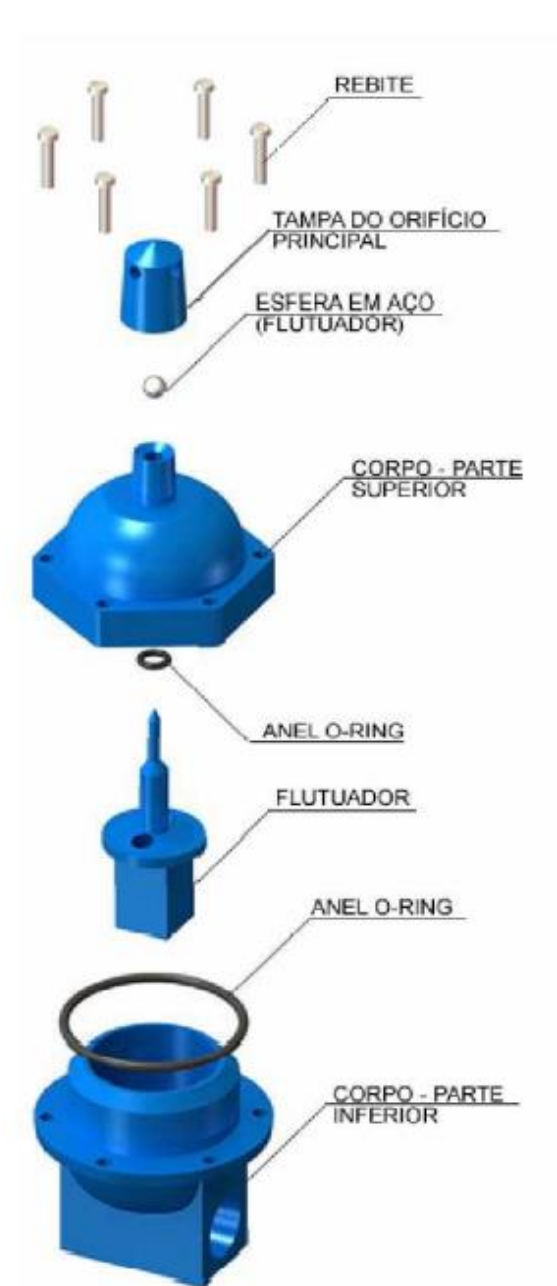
Vista explodida do eliminador de ar 3/4" modelo "B".
